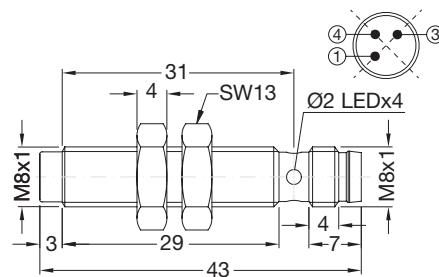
Kurze Ausführung, Nicht bündiger Einbau, Steckversion
